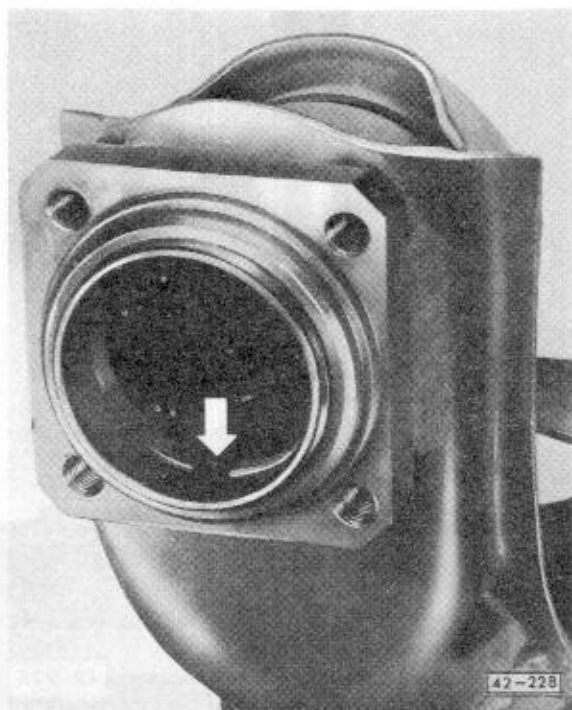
Zylinderrollenlager, Außenlaufring mit Dorn austreiben
